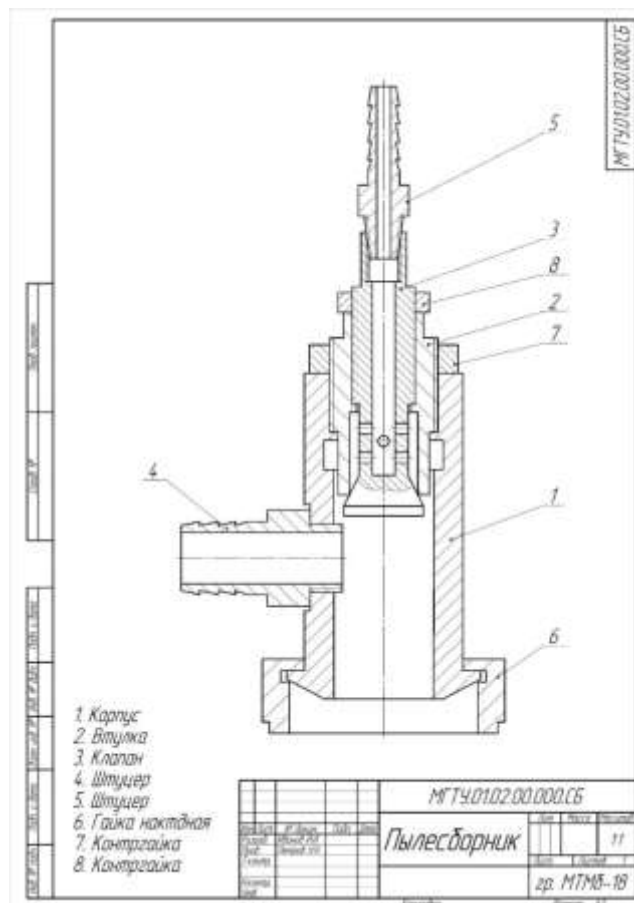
Сборочный чертеж пылесборника инжекторного, используемый в качестве метки для AR-приложения
